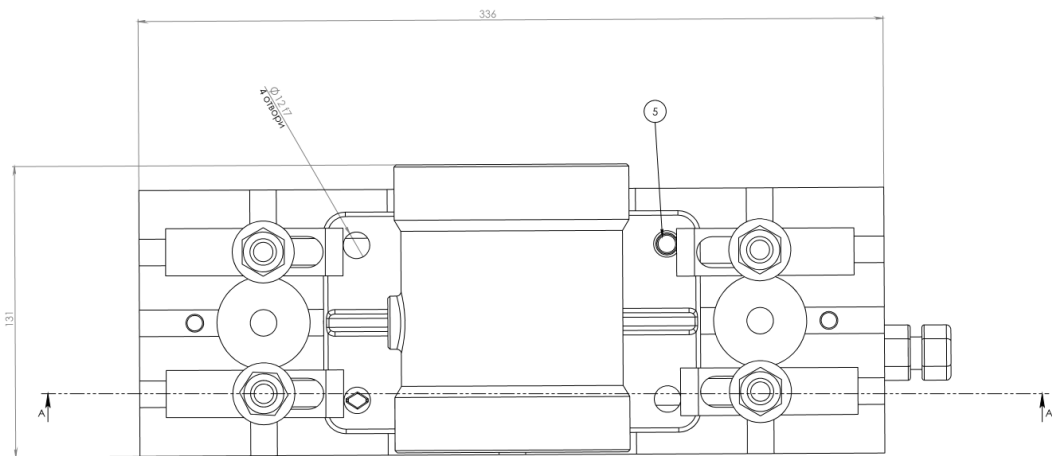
Пристрій для обробки на 015 операції.
